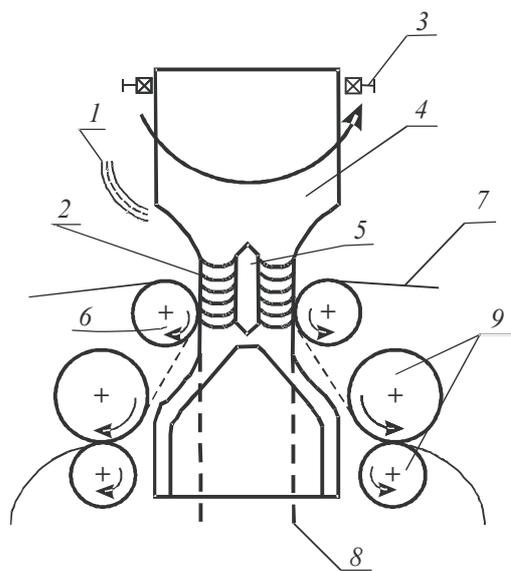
Установка для получения нитей с разрезным ворсом
